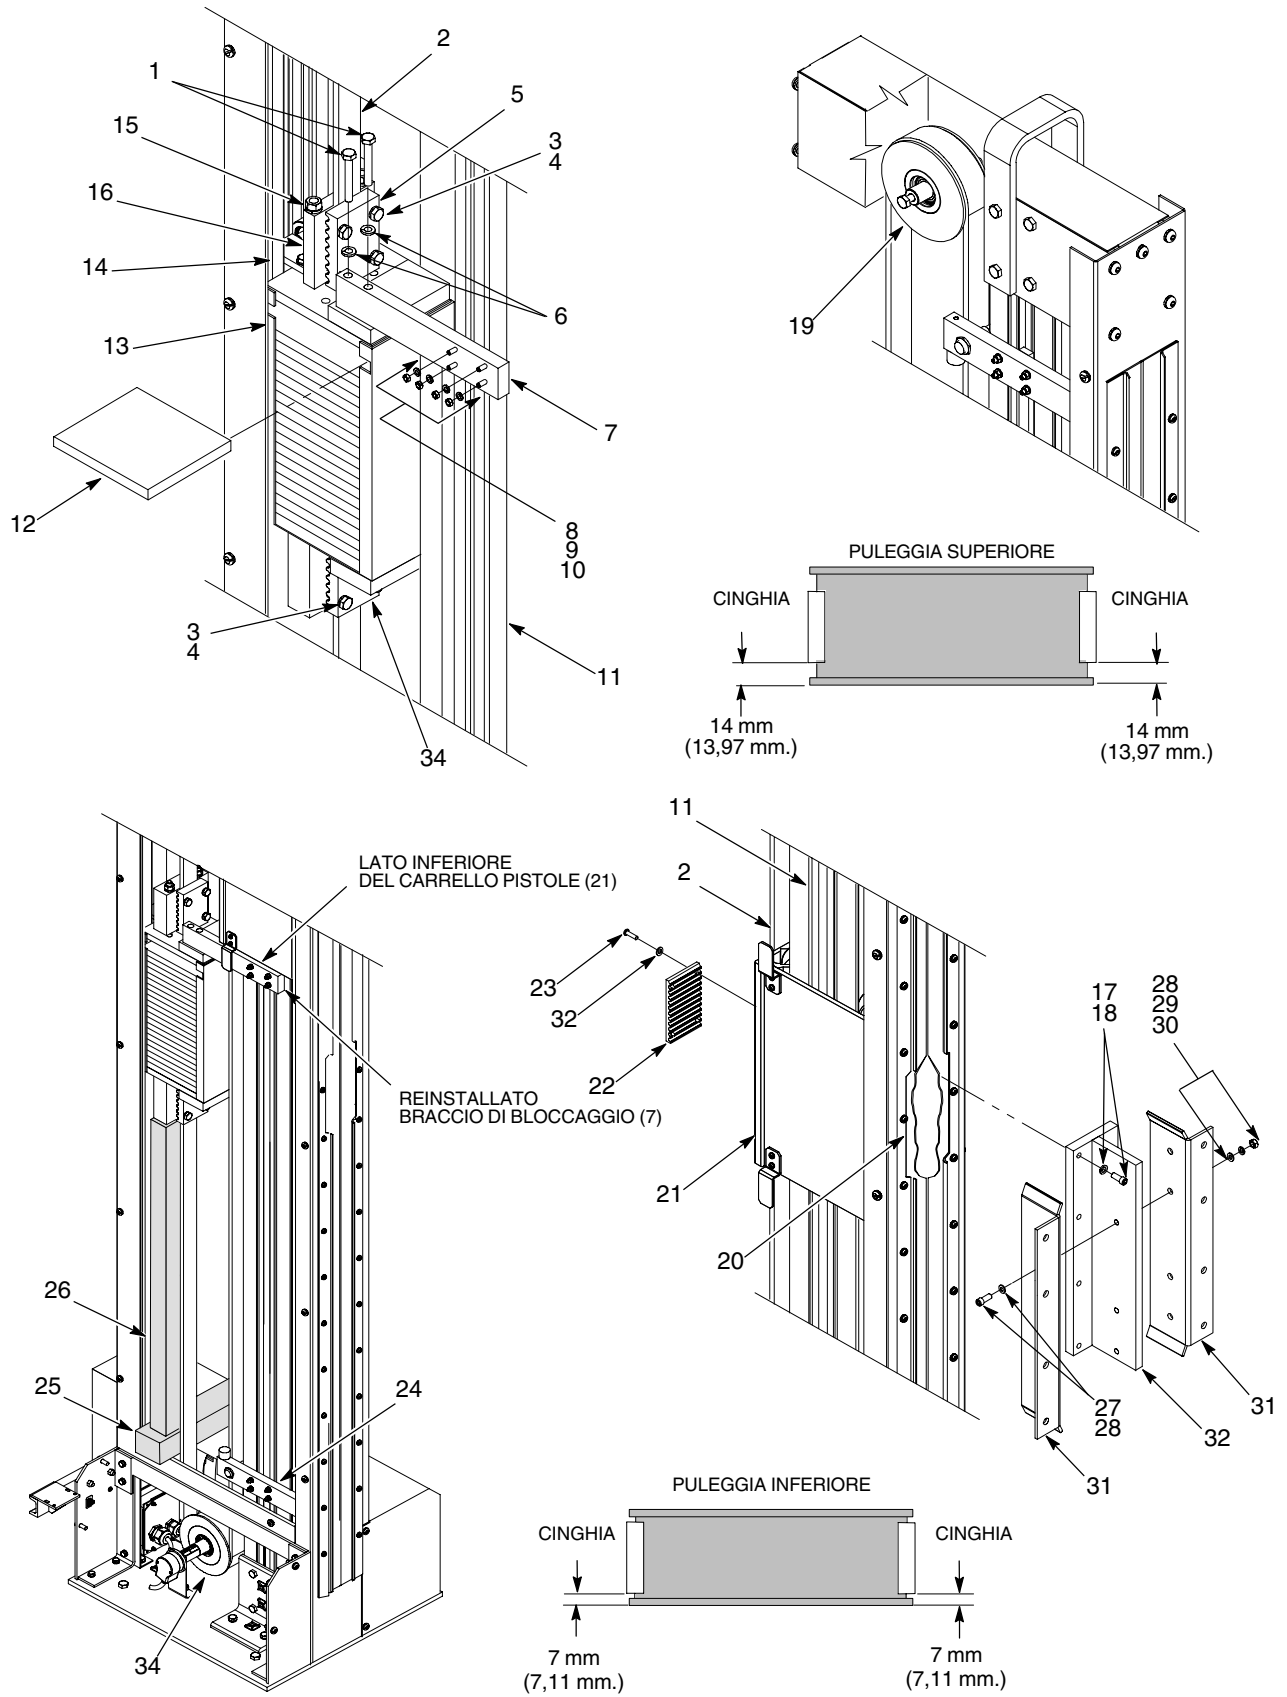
Installazione del dispositivo di montaggio del carrello pistole
